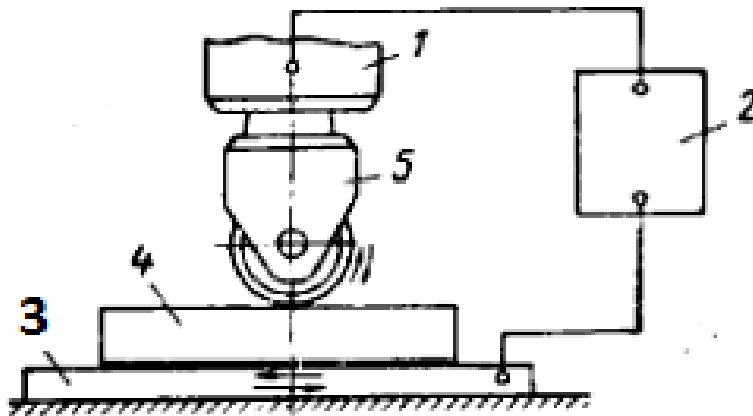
Схема обробки плоских деталей на фрезерному верстаті:
